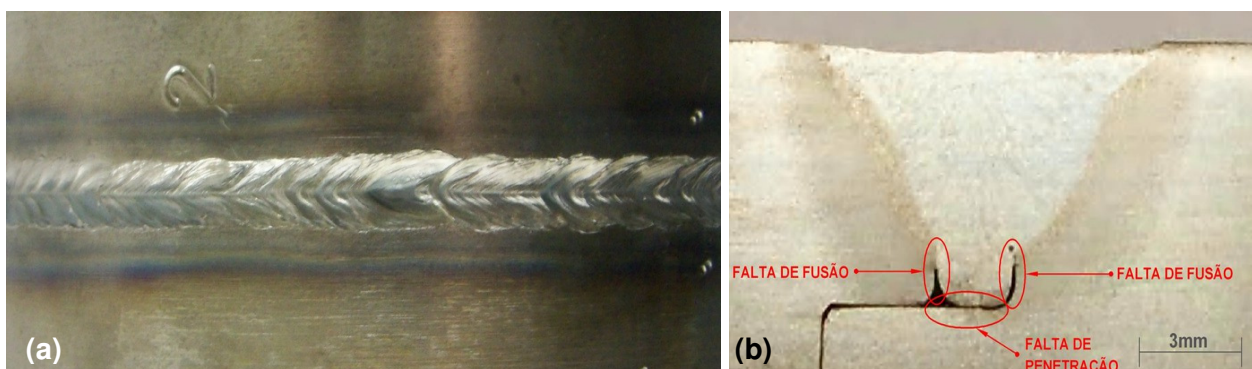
Tambor enrolador – corpo de prova 2. a) inspeção visual; b) análise macrográfica
